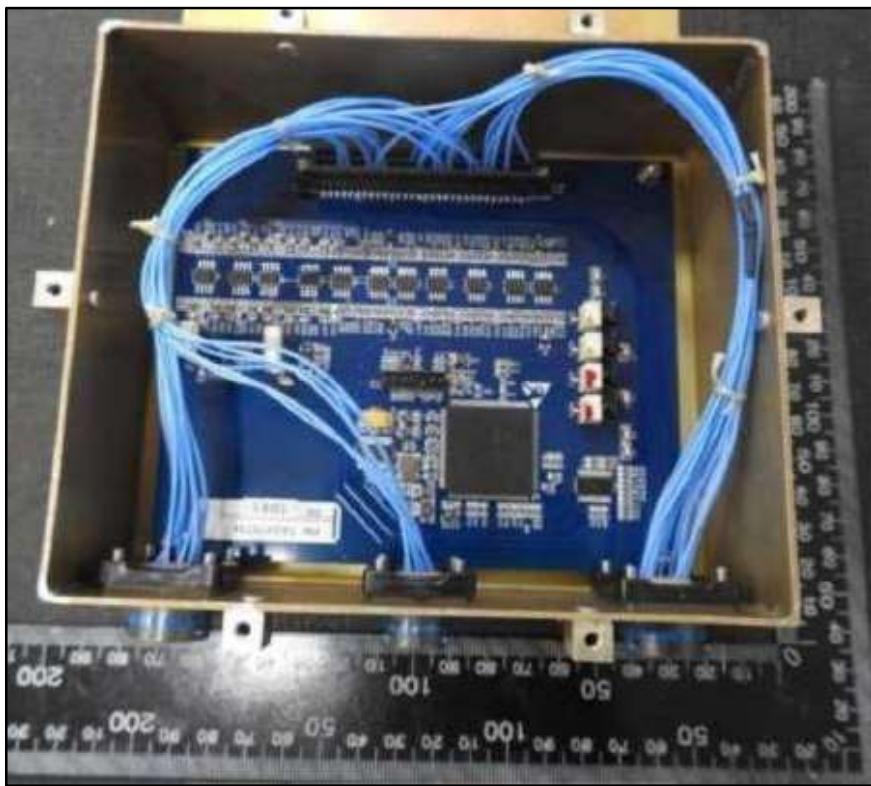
Содержимое Блока управления двигателем Engine Control Unit (ECU)
